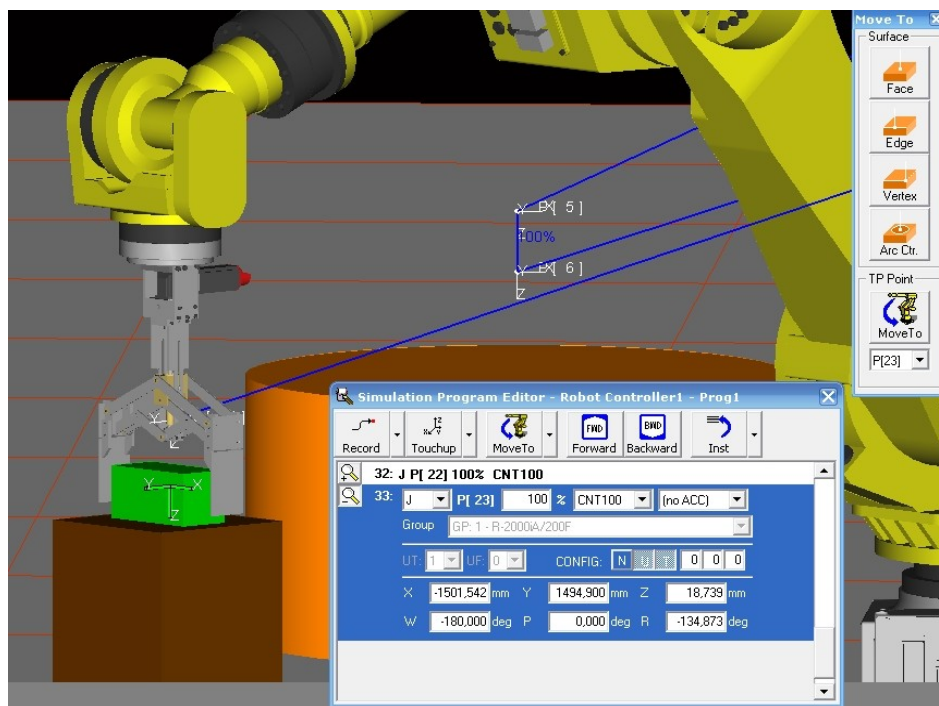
Definición de posición para capturar "Pieza1" en "Fixture2".
